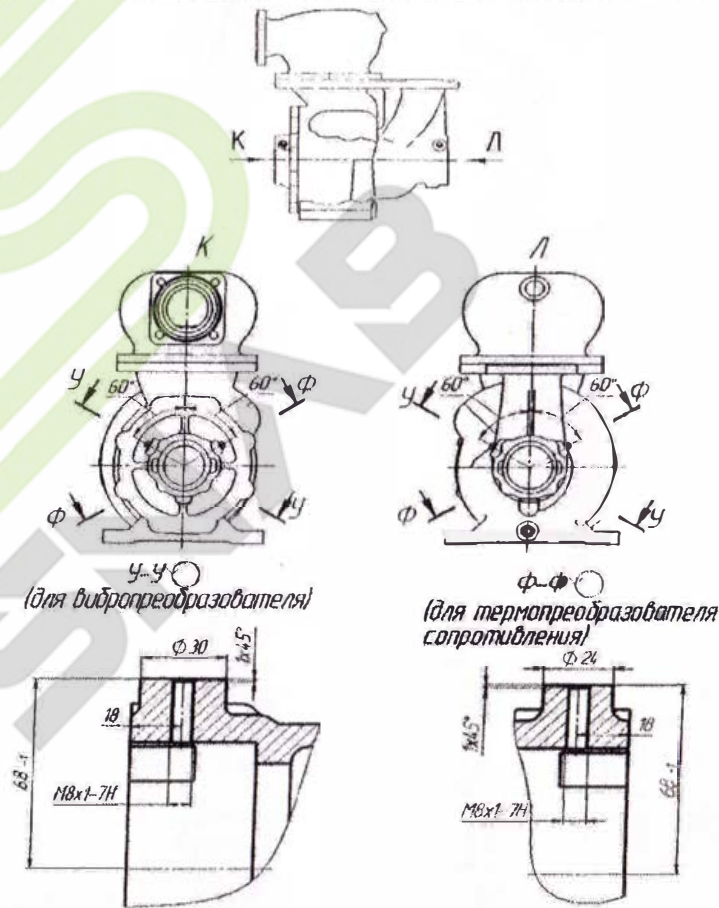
Расположение и присоединительные размеры для установки датчиков подлинников насоса
